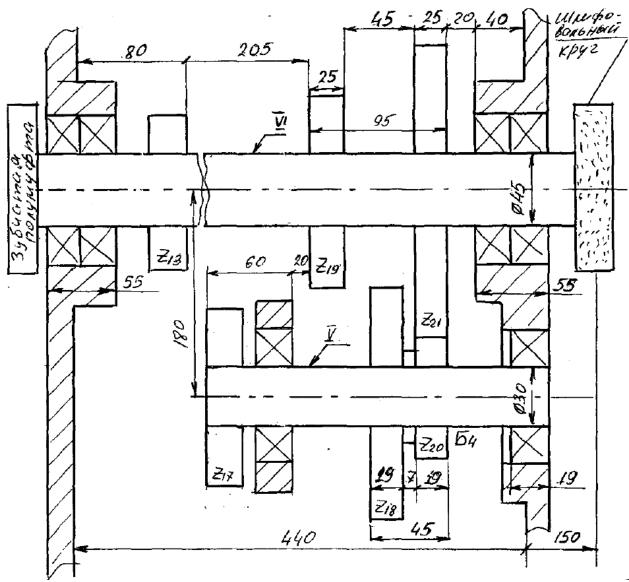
Компоновочная схема развертки наиболее нагруженной группы передач
